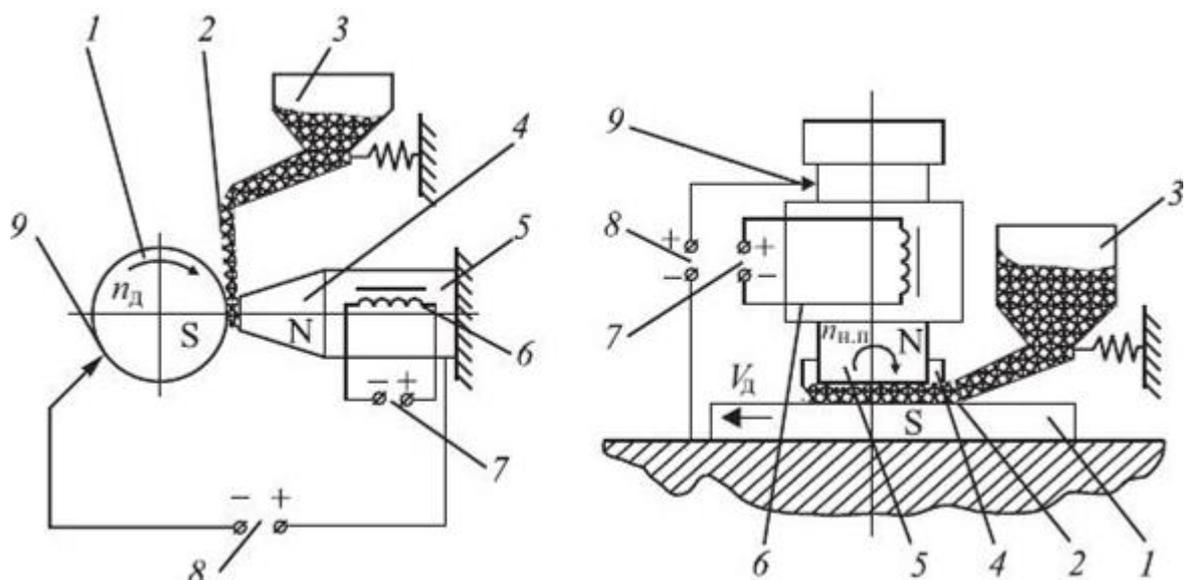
Принципиальная схема электромагнитной установки на поверхность заготовки детали типа тела вращения (слева) и плоские поверхности (справа): 1 – заготовка детали; 2 – ферромагнитный порошок; 3 – бункер-дозатор; 4 – полюсный наконечник; 5 – сердечник электромагнита; 6 – электромагнитная катушка; 7 – источник питания электромагнитной катушки; 8 – источник технологического тока; 9 – скользящий контакт плоской поверхности.
